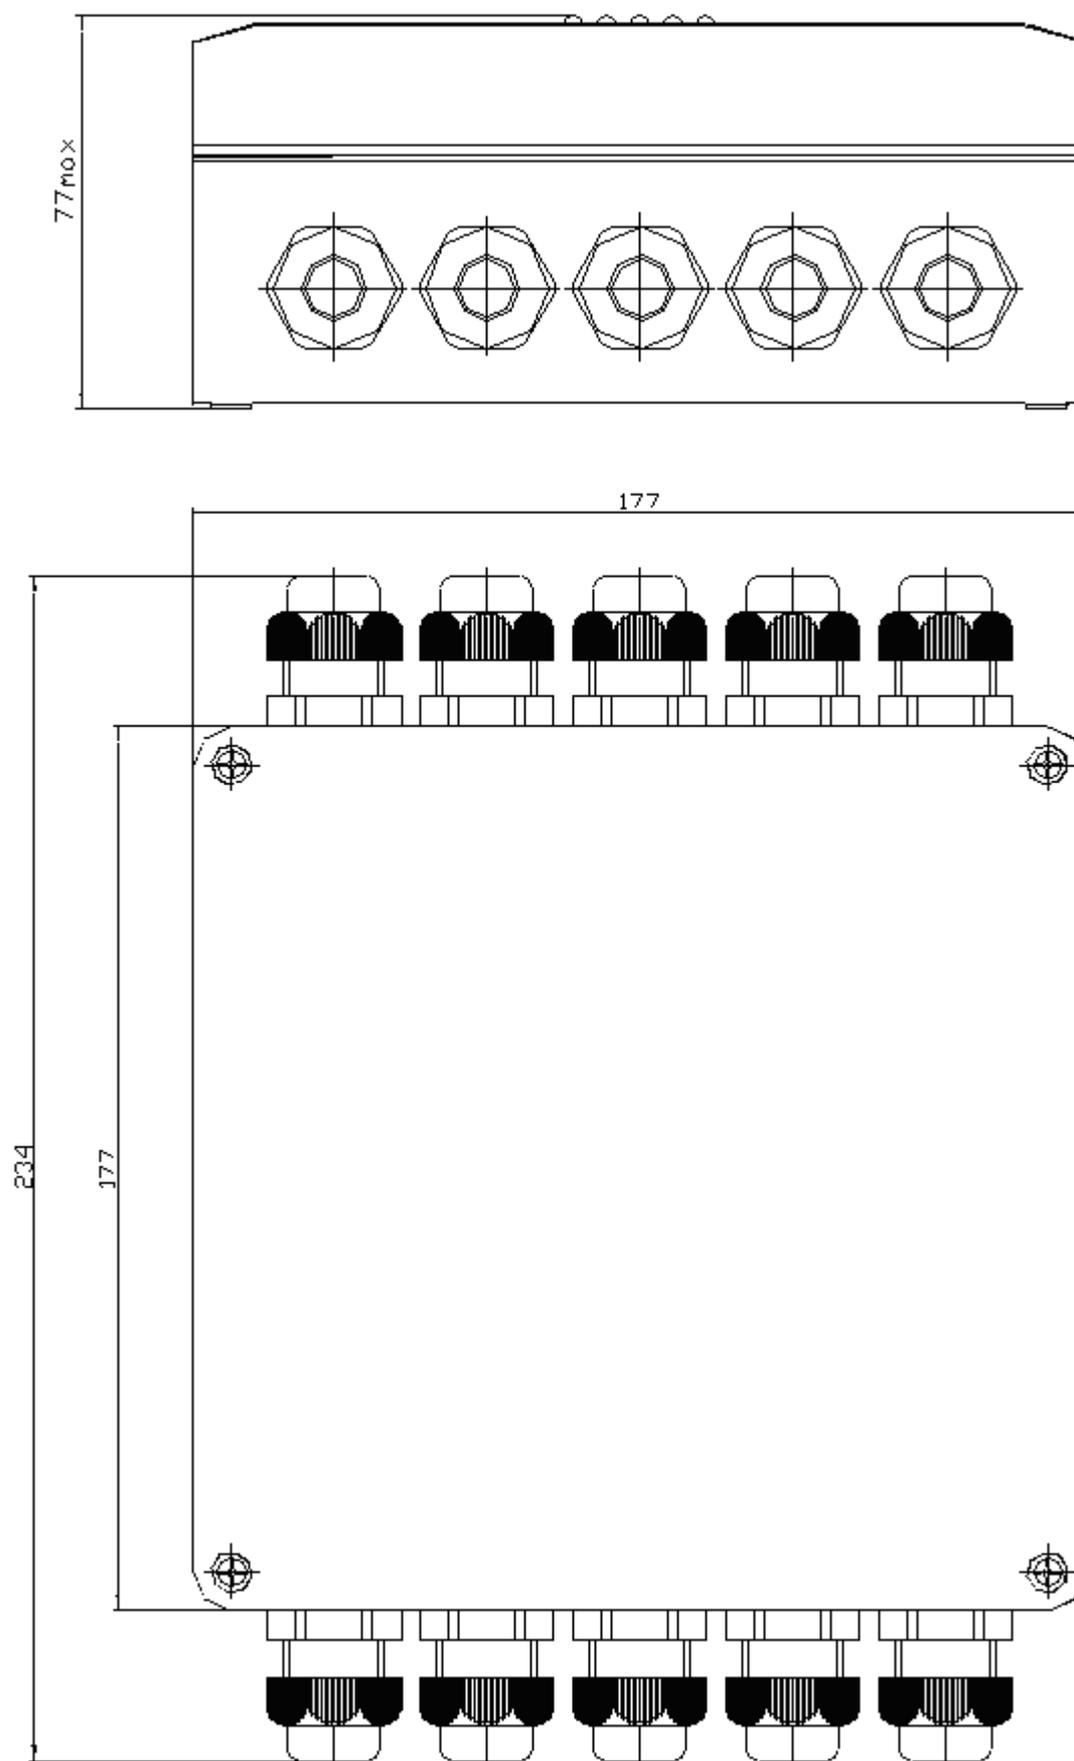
Габаритный чертеж исполнения МС-АП-01-00-01
